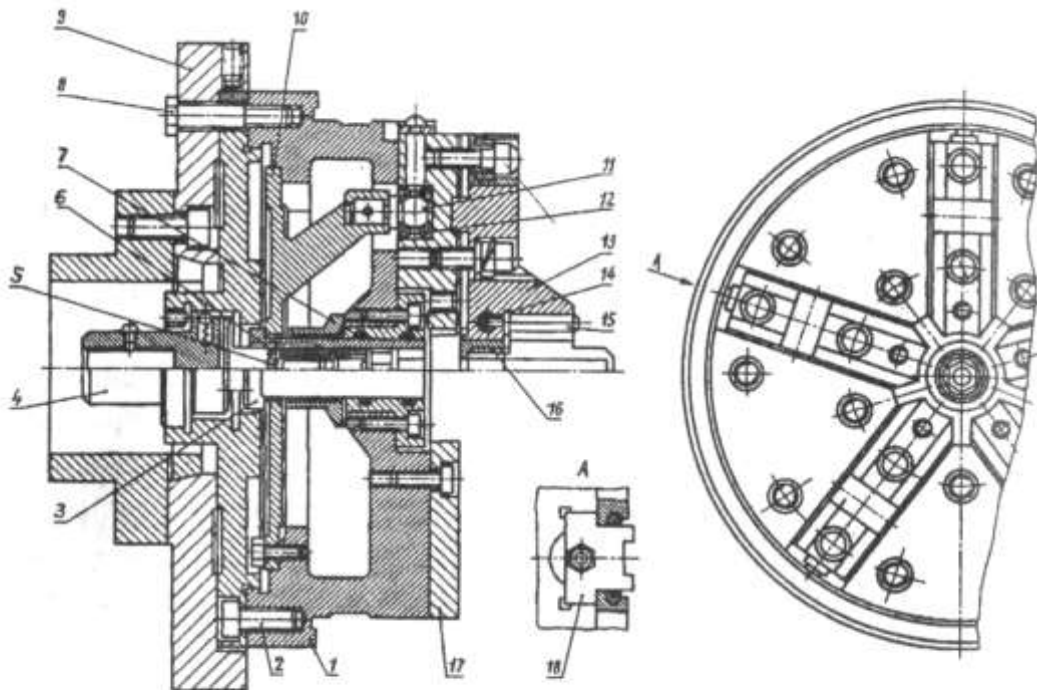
Мембранный патрон для шлифования центрального отверстия в прямозубых зубчатых колесах
